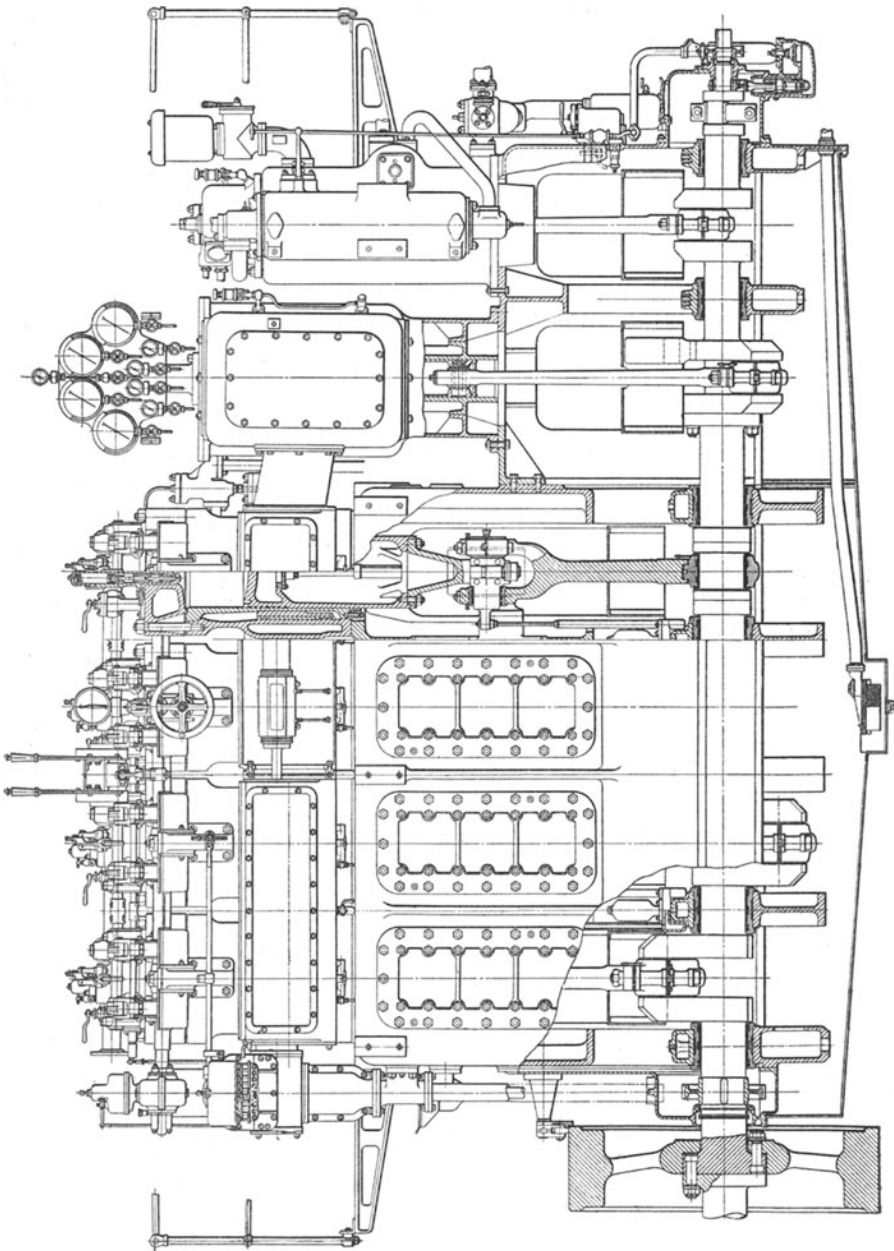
4-zylindrige Stephen-Sulzer Zweitaktmaschine.
